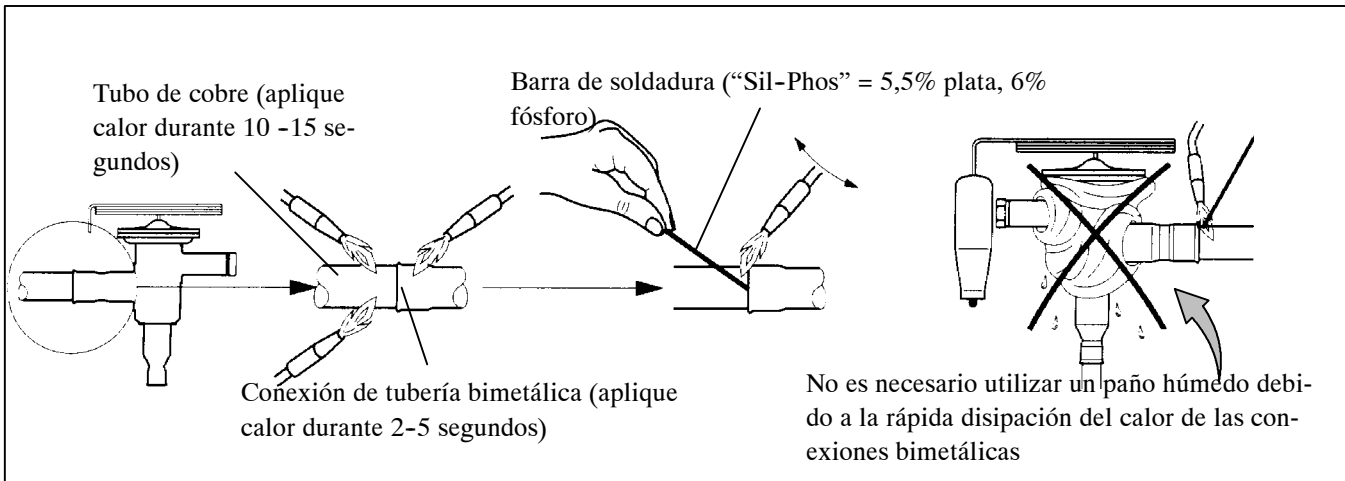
Procedimiento de Soldadura de la Válvula de Expansión Termostática
